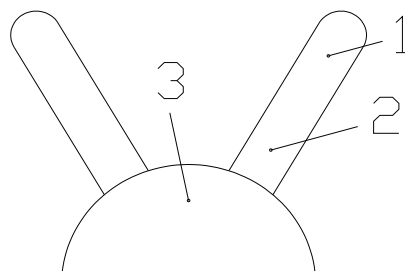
Образец, отлитый в кокиль «рожковой» формы
